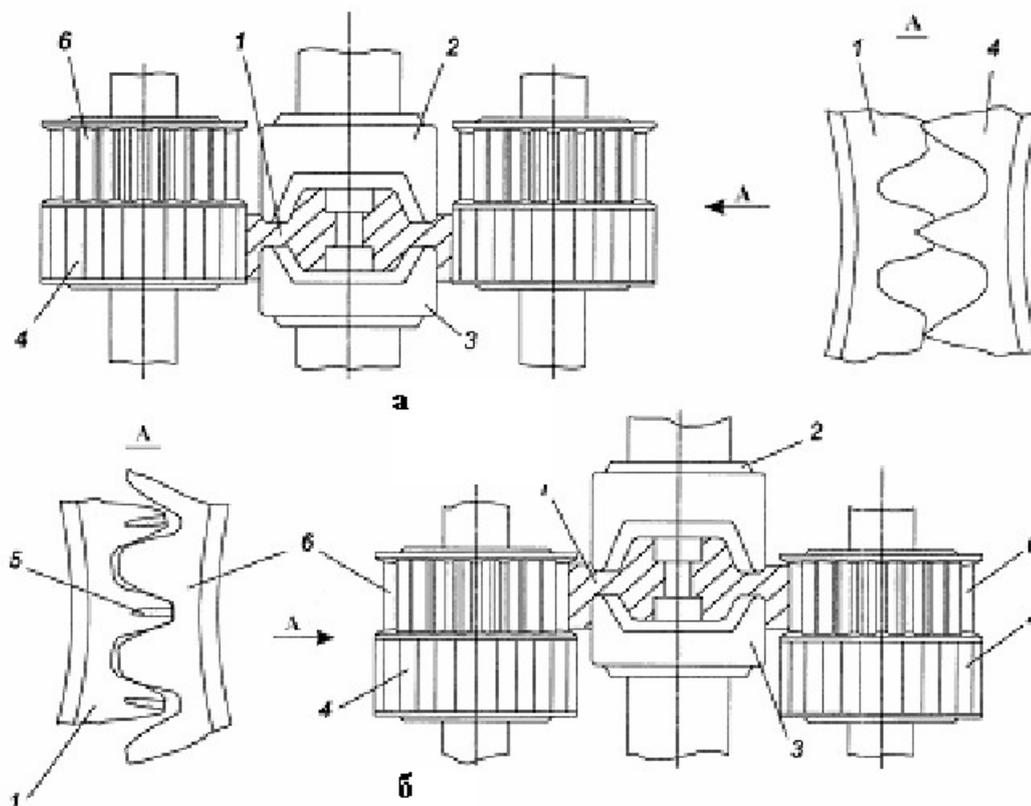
Схема устройства с двумя парами зубчатых роликов:
